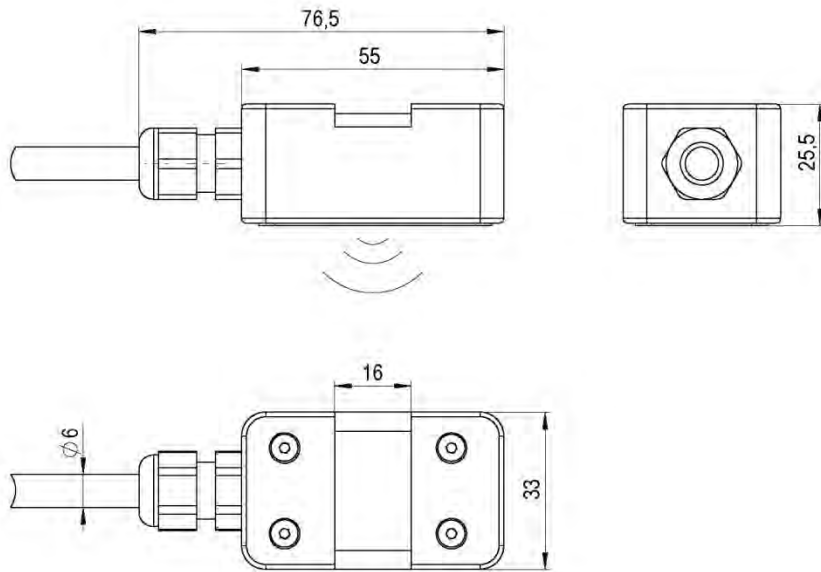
Maßzeichnung Clamp-On Sensor Typ NIC-CO01
